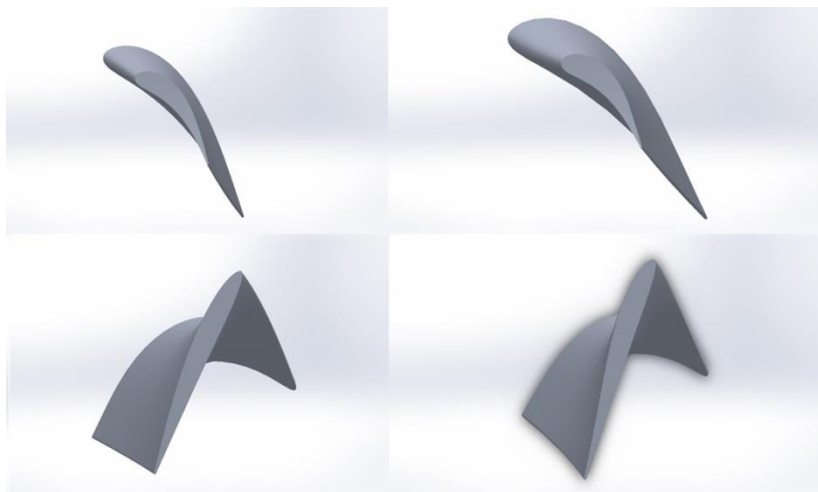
3D модели сопловой и рабочей лопатки 3 и 4 ступени
